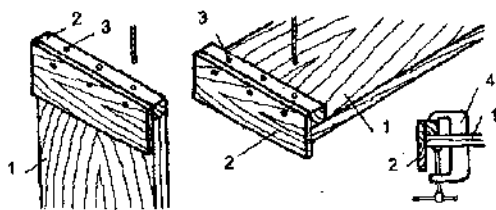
Шаблон для сверления торца и плоскости заготовки: 1 — заготовка; 2 — шаблон; 3 — отверстие а шаблоне; 4 — струбцина, к которой крепится шаблон
